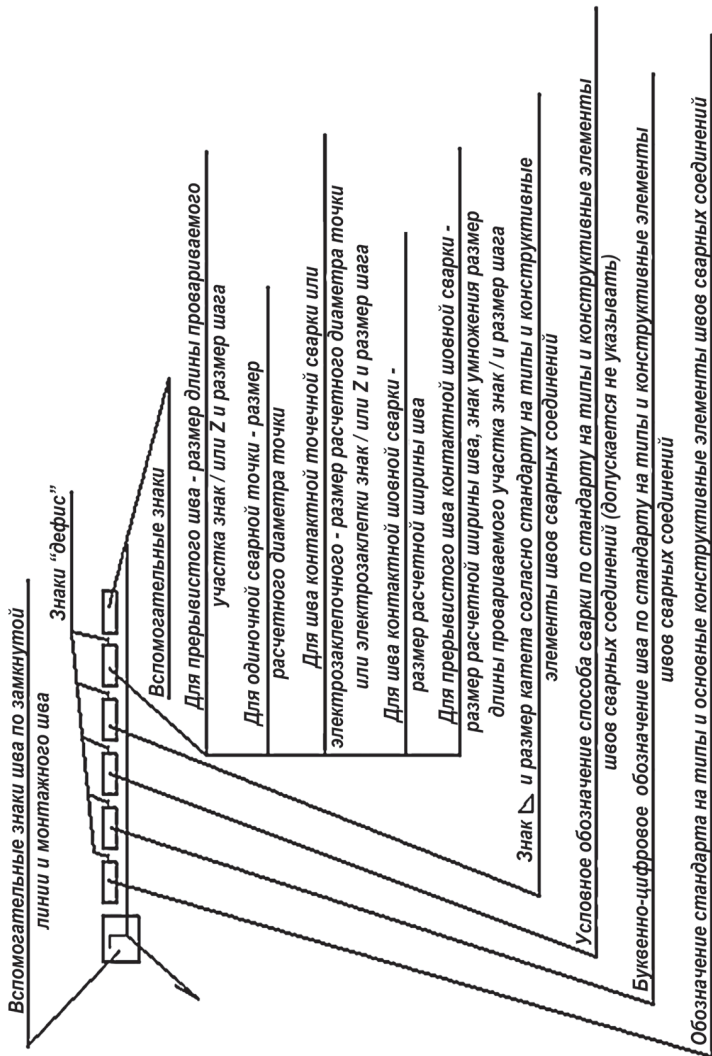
Схема структуры условного обозначения стандартного шва
